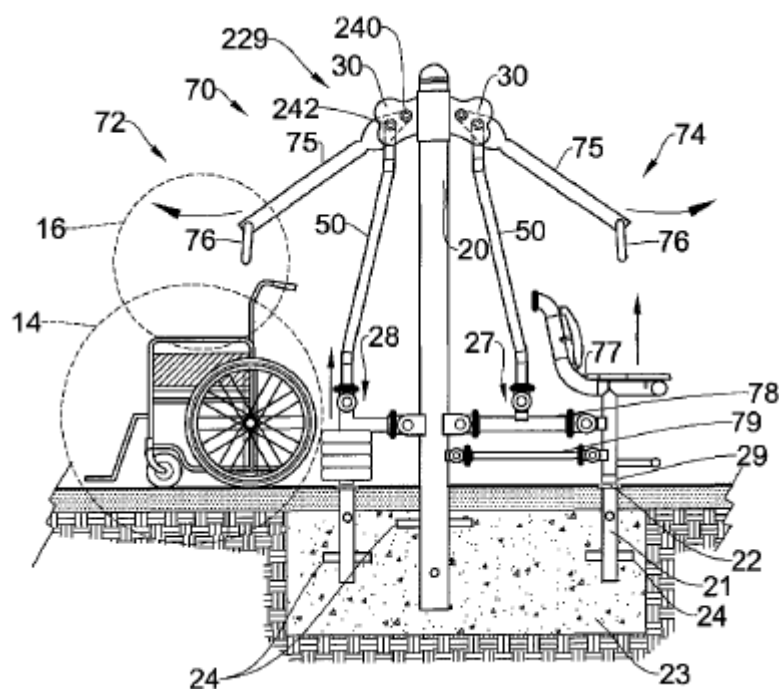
Equipamento de ginástica proposto por Mendelsohn, 2015.
